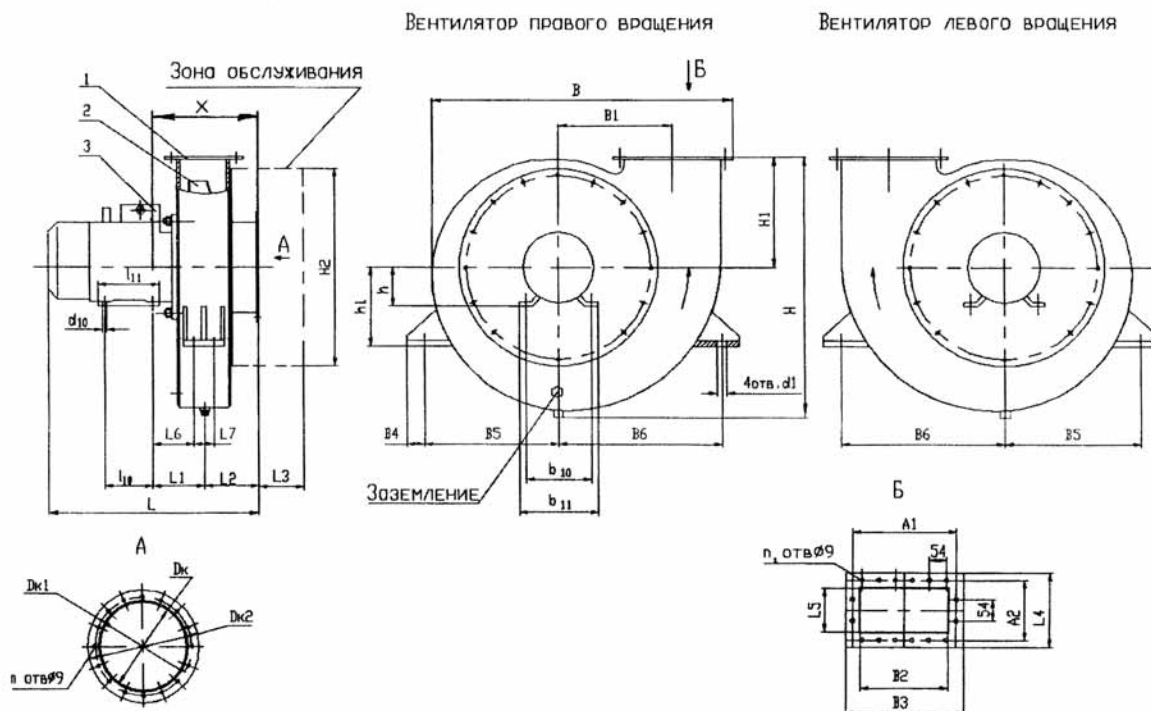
1 – корпус; 2 – колесо; 3 – двигатель
